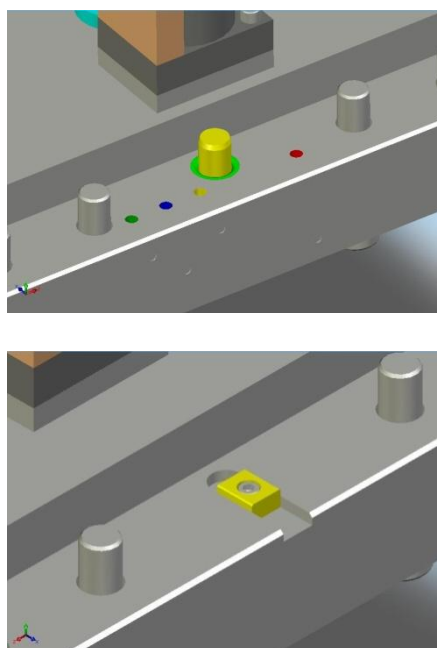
Pormenor da chaveta e cavilha de posicionamento da mesa
